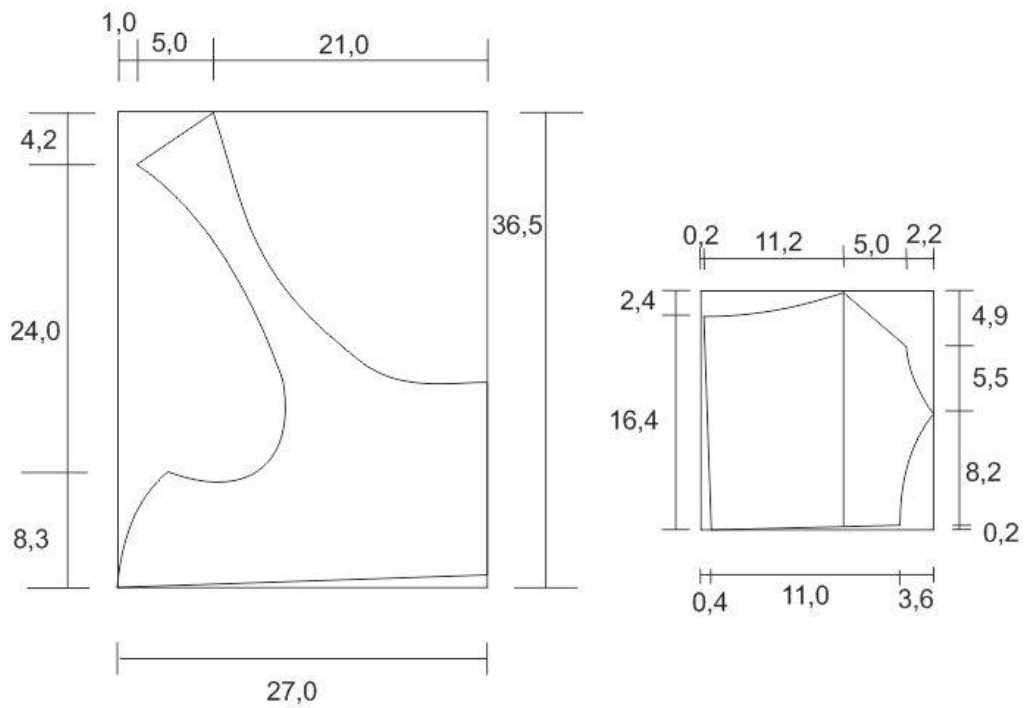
Peça do molde do corpo. Fig. 227 - Peça do molde do corpo.
